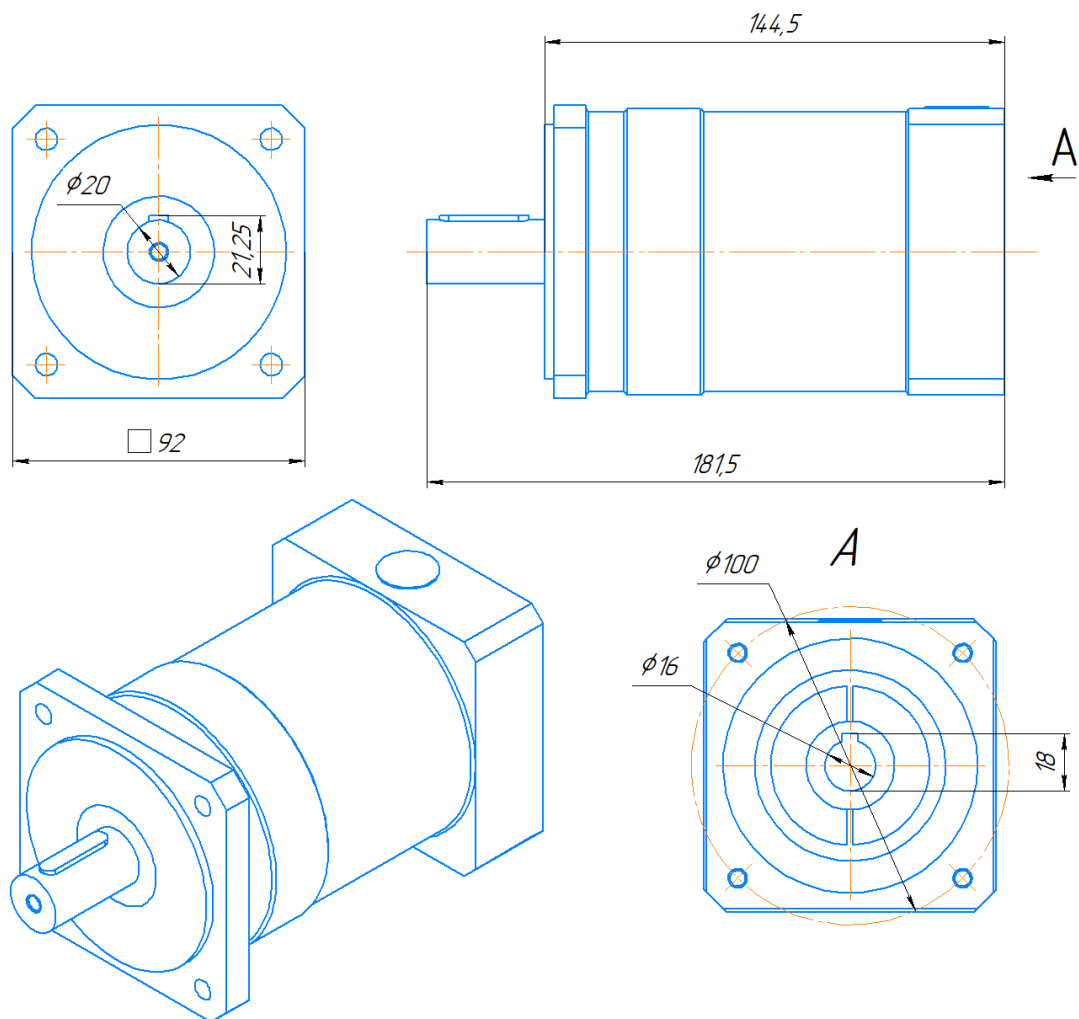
Редуктор планетарний TF080 [26].
